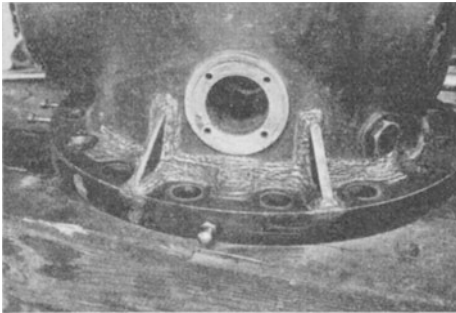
Geschweißtes Stahlgußgehäuse.
